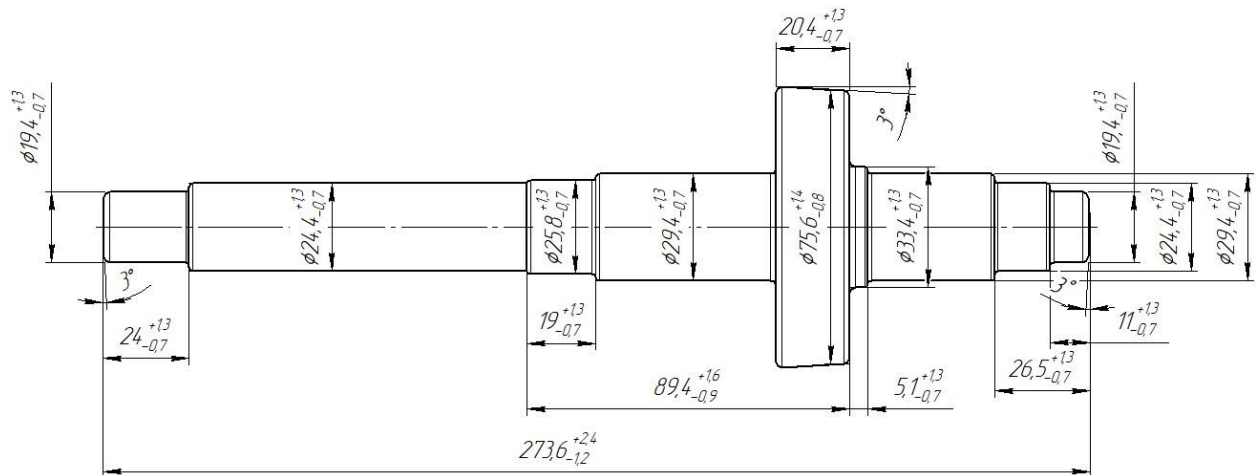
Штамповка детали «Фланцевый вал»
